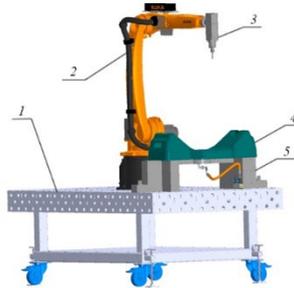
Модель роботизированной ячейки. 1 – сварочный стол, 2 – робот-манипулятор, 3 – инструмент с фрезой, 4 – обрабатываемая деталь, 5 – технологическая оснастка.
